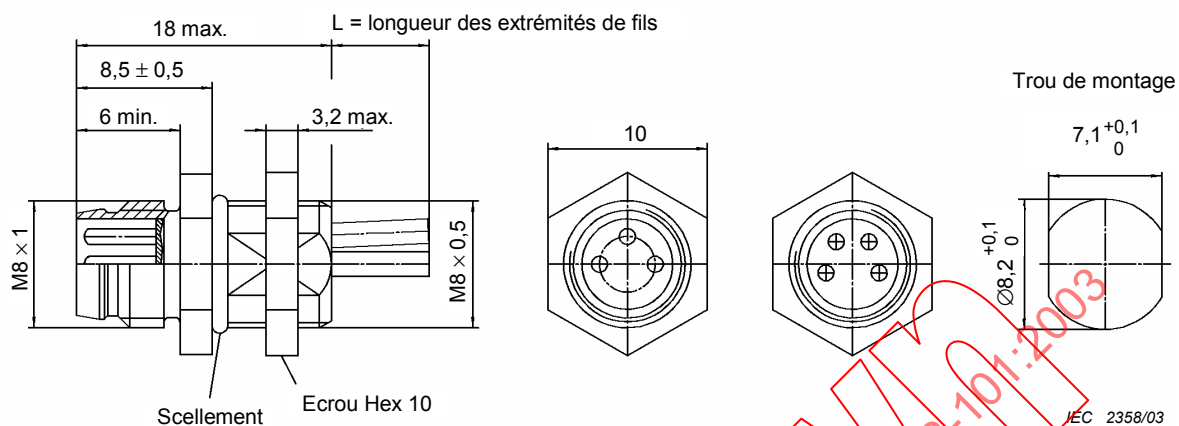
Embase avec extrémités de fils, montage arrière par écrou, contacts mâles
